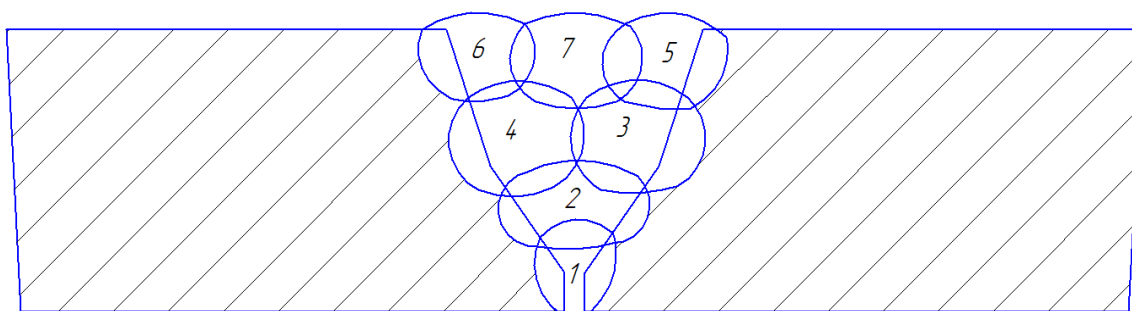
Сварка облицовочного слоя шва
